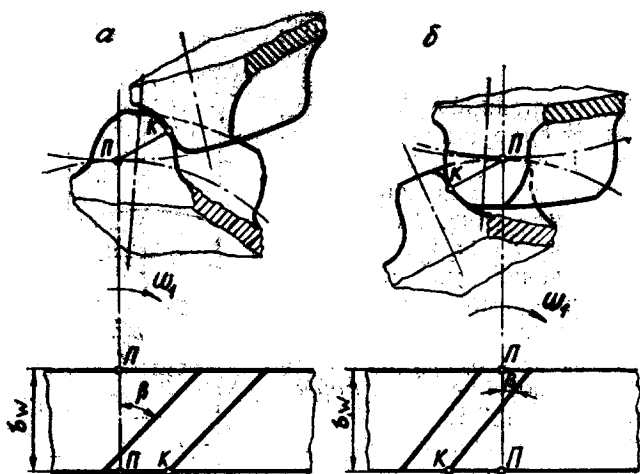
Сопряженные зубчатые колеса одноточечного зацепления:
